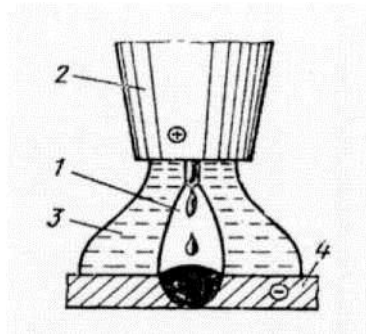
Схема зварювання стикових поздовжніх швів
